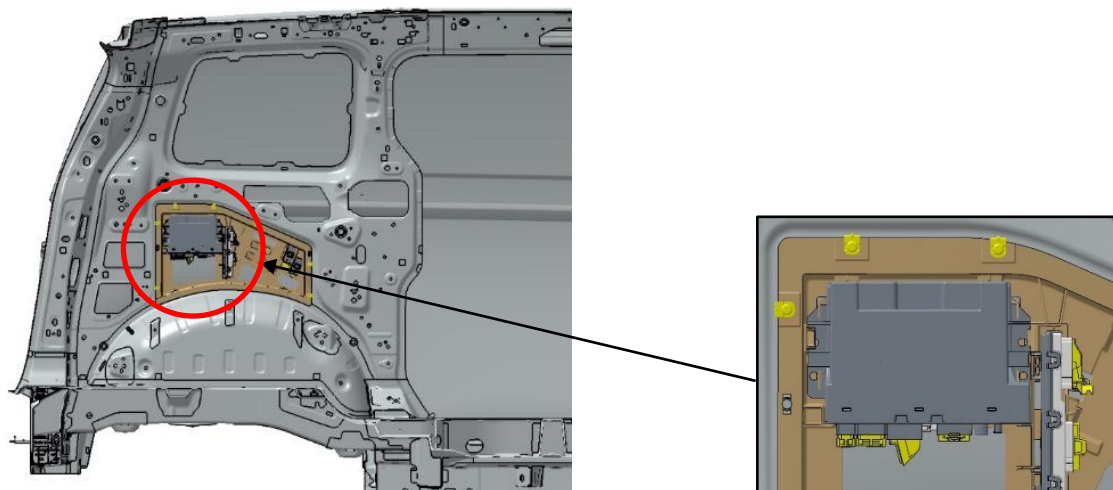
position de montage du KFG derrière le revêtement de la paroi latérale, au-dessus du passage de roue arrière gauche
